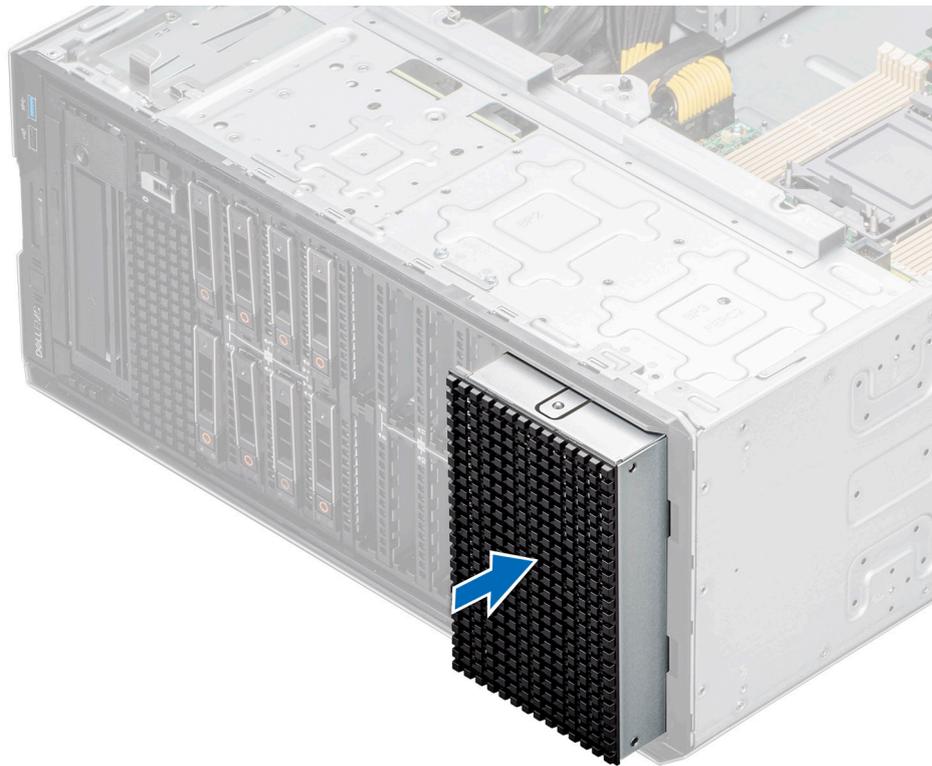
Installieren des Platzhalters für das Laufwerkschachtgehäuse
